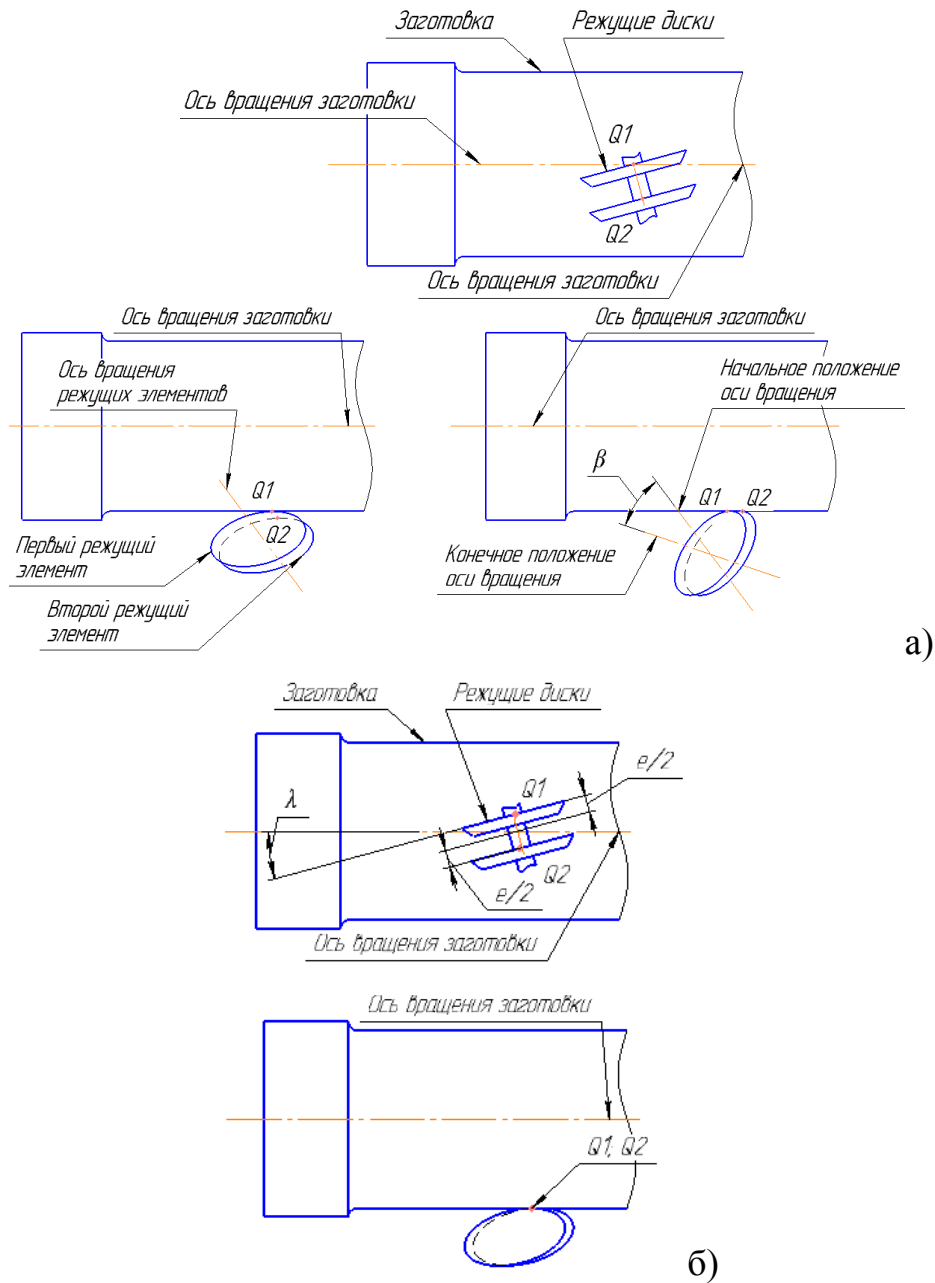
Схема установки режущих дисков относительно оси вращения заготовки
